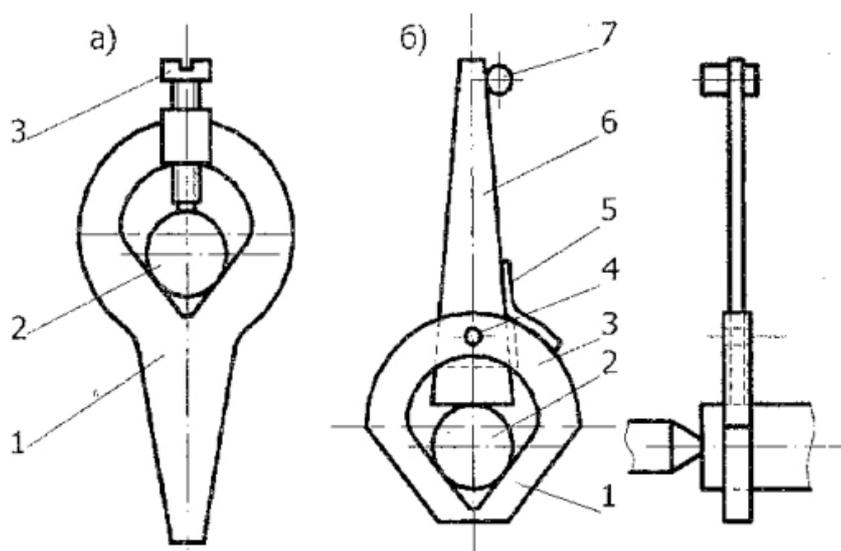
Конструкции хомутиков: а – обычный; б – самостягивающийся;
